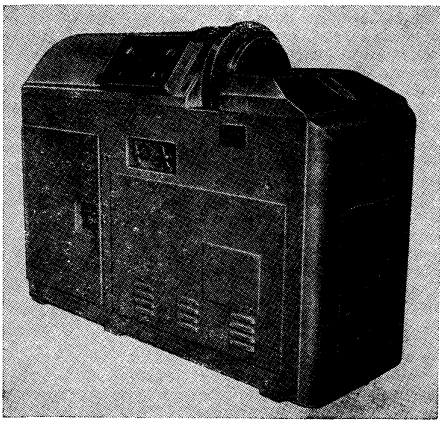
Полуавтомат для сварки трением типа МСТ-35-5 (ВНИИЭСО)
